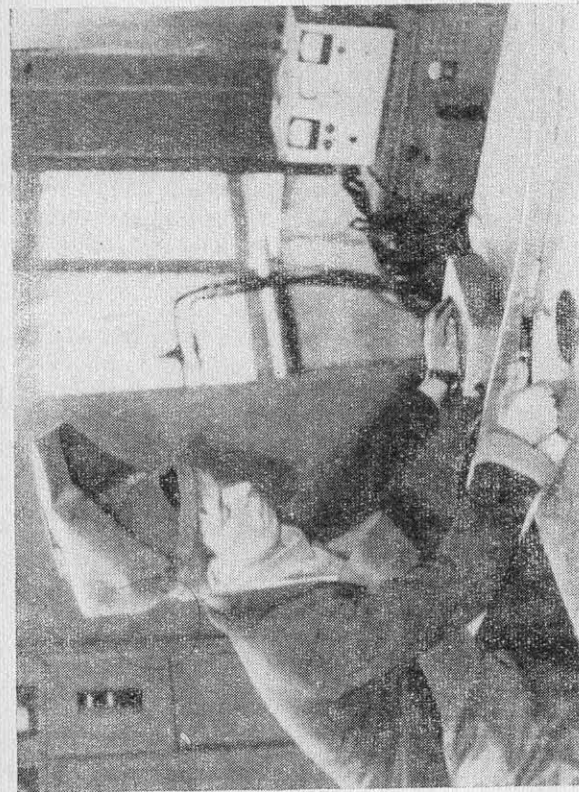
Сварка узлов набора полуавтоматом «Спутник».
